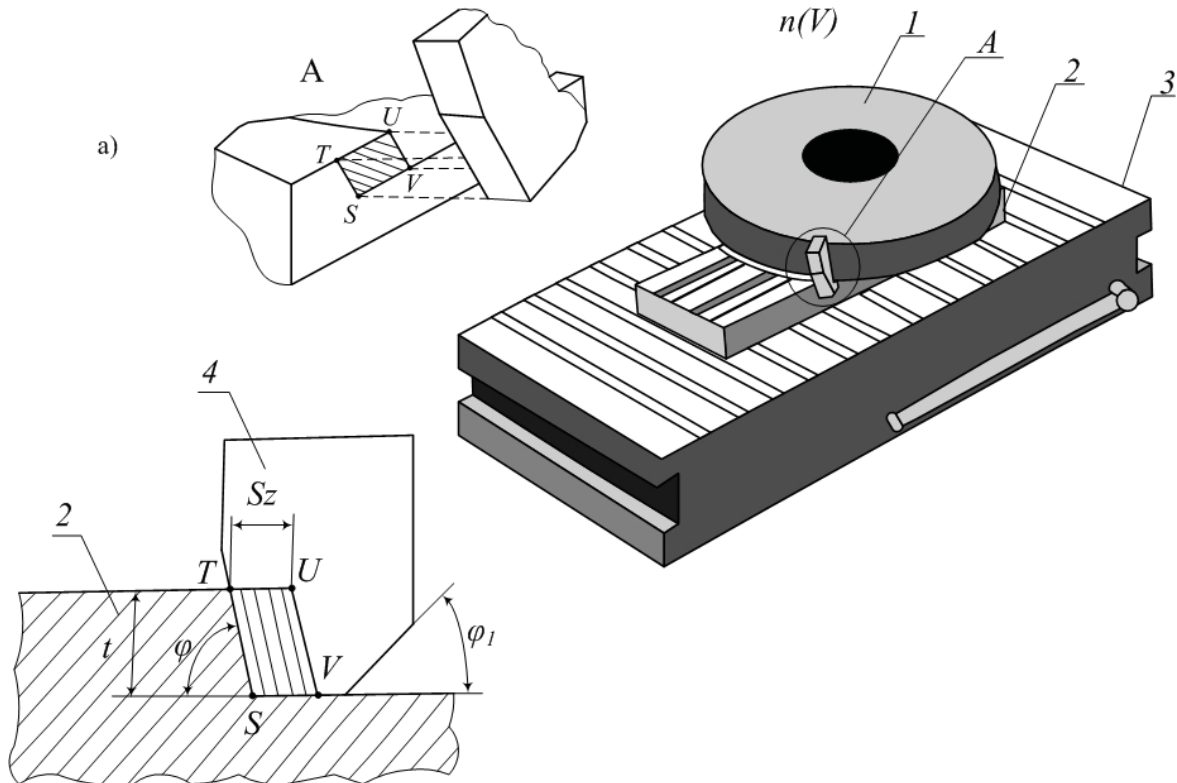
Схема торцового фрезерования и условия первоначального контакта режущей части инструмента с обрабатываемой поверхностью инструмента: 1 – торцовая фреза; а – схема врезания зуба в обрабатываемую поверхность заготовки; 2 – заготовка с продольными пазами; 3 – магнитная плита для закрепления заготовки и установки ее на станке; 4 – зуб фрезы; t – глубина резания, мм
